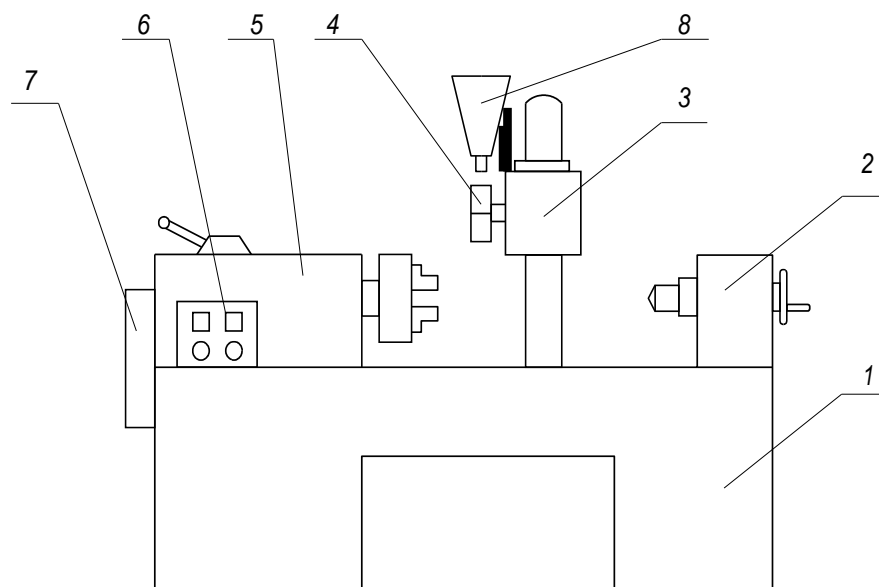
Принципова схема установки для наплавлення під шаром флюсу:
